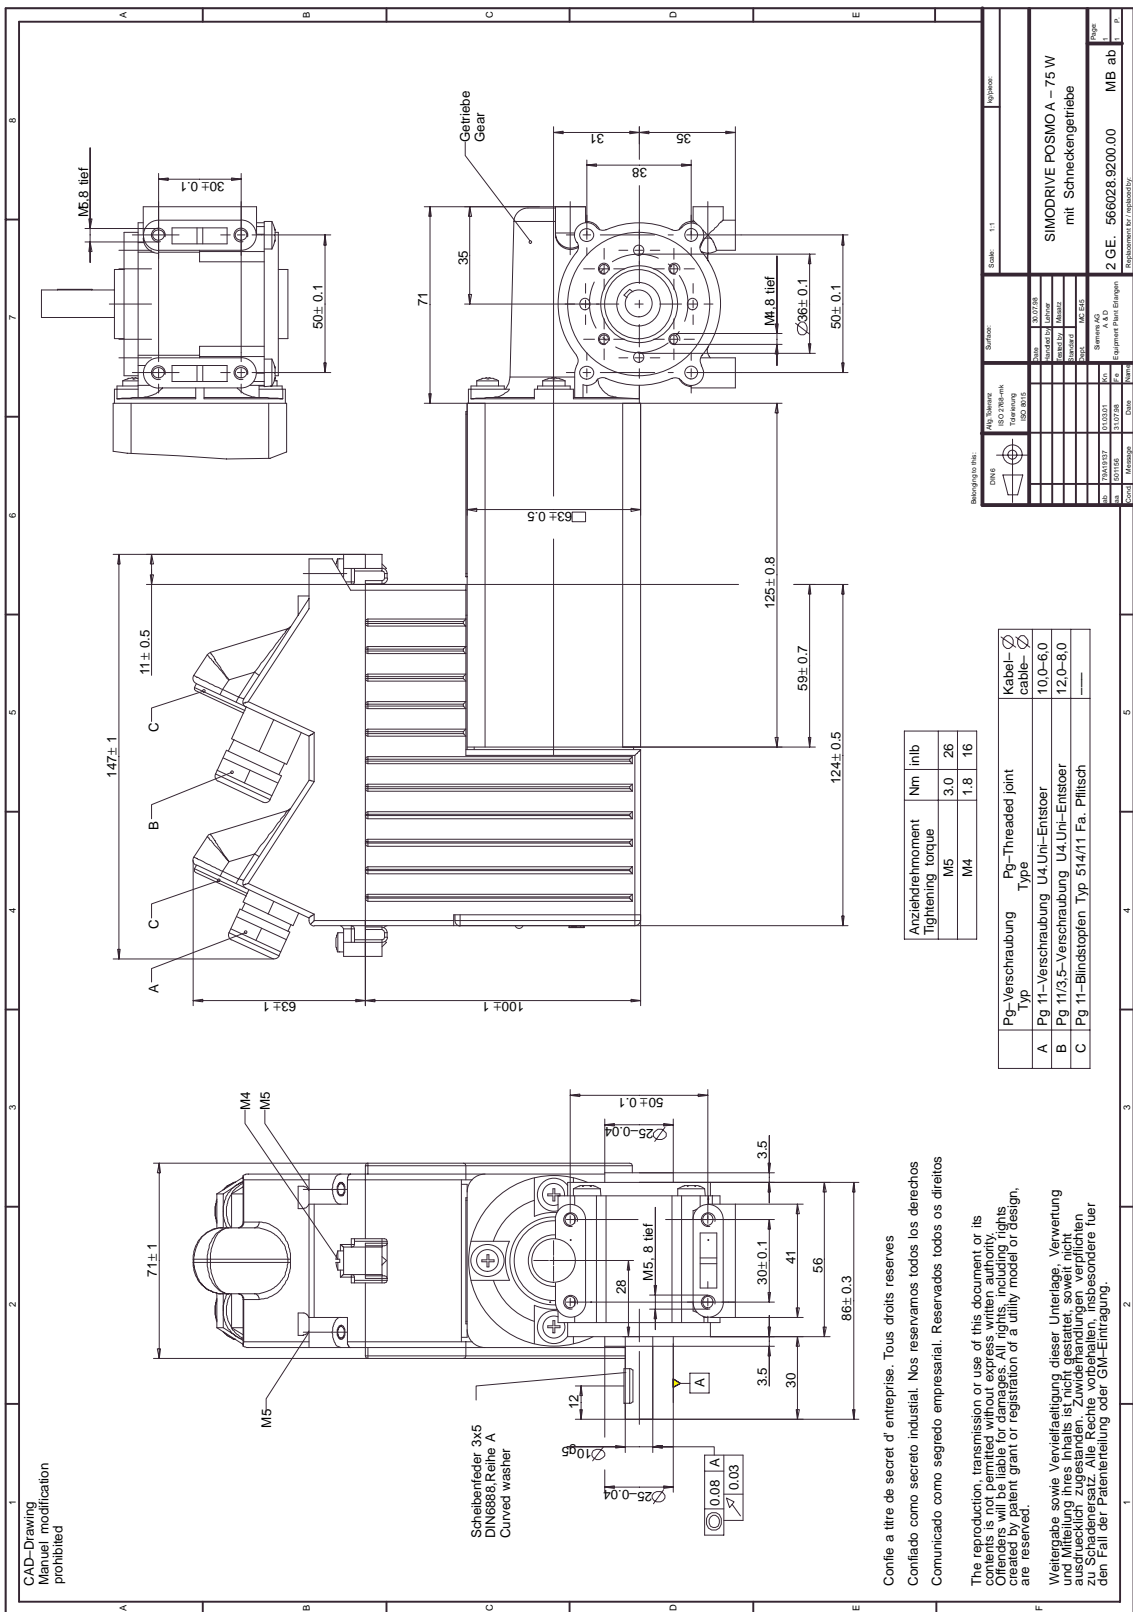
Maßblatt: SIMODRIVE POSMO A – 75 W mit Schneckengetriebe
